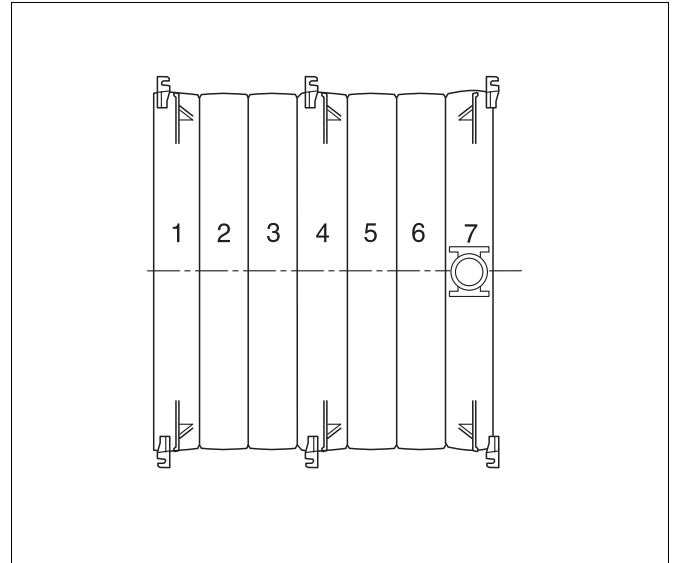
Draufsicht: Kesselblock (7 Kesselglieder) mit Konsolen
